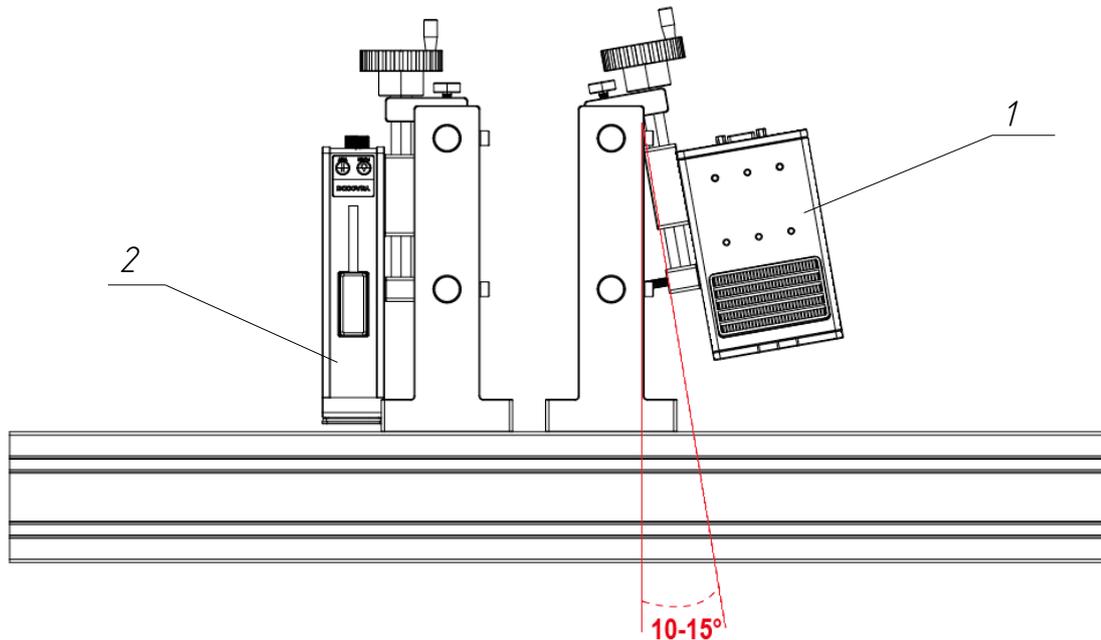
Установка УФ-лампы под углом к плоскости печатающей головки. Условные обозначения: 1 — УФ-лампа; 2 — печатающая головка.
